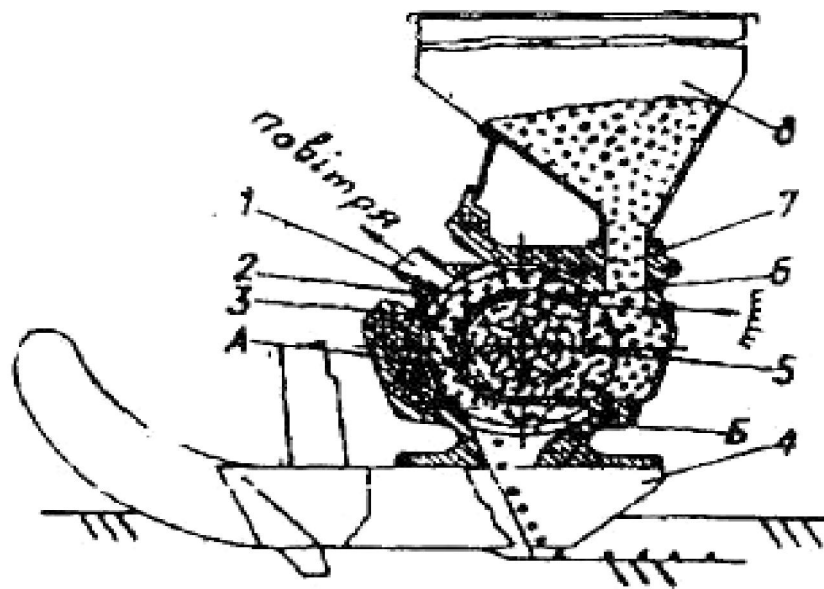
Схема пневмо-механічного висівного апарата з вертикальним плоским диском: 1 - капронова вставка; 2 - кришка з пневматичною камерою; 3 - висівний диск; 4 - сошник; 5 - ворушила; 6 - відбивач зайвого насіння; 7 - корпус; 8 - бункер; А - зона розрідження; Б - зона атмосферного тиску
